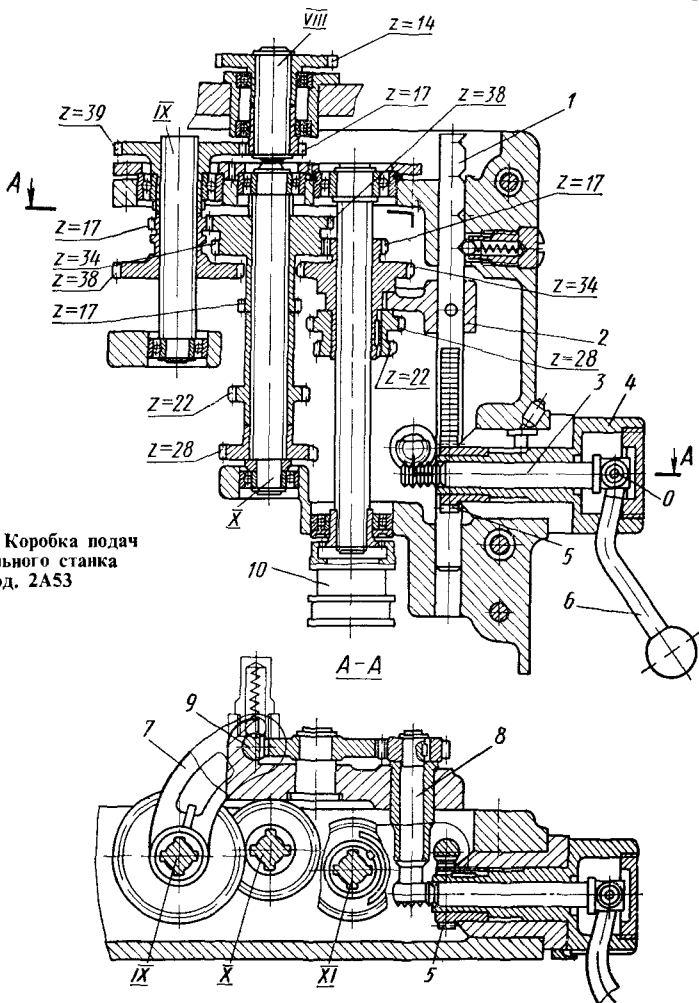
Коробка подач сверлильного станка мод. 2А53
